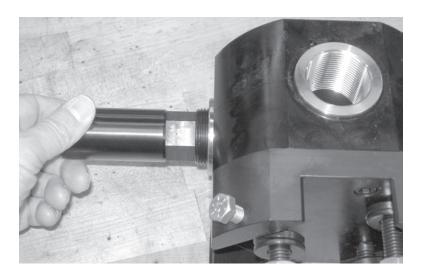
Вверните кулачки в корпус зажимного патрона.
